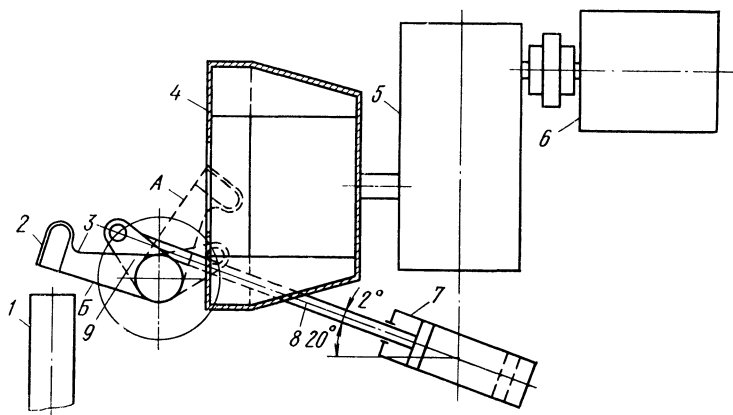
Схема установки для механизированной подачи порошкообразной смазки в гильзу [438]
